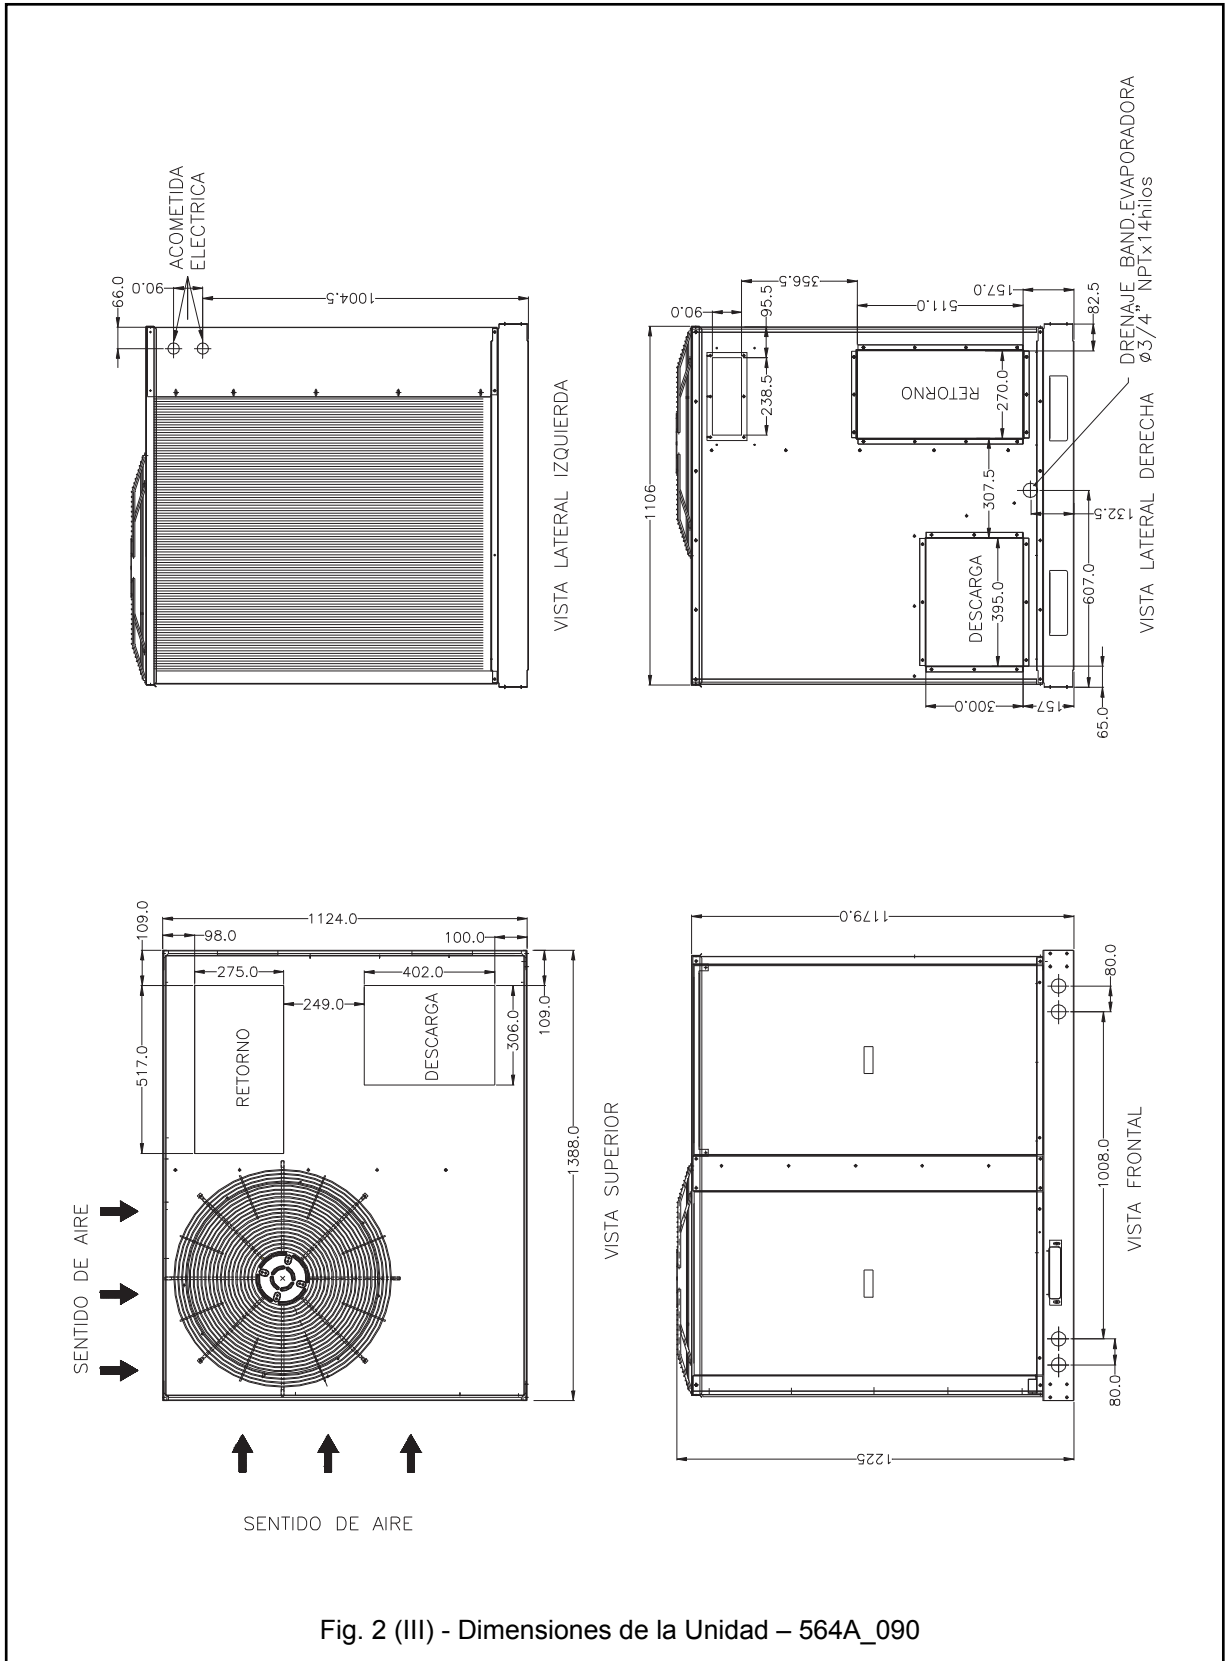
(III) - Dimensiones de la Unidad – 564A_090
